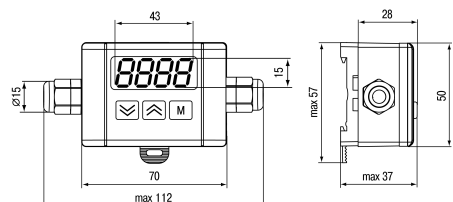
Габаритные размеры корпуса НЗ
